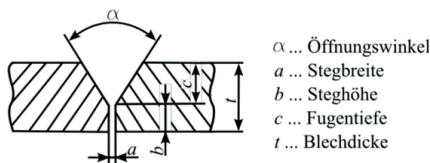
Nahtgeometrie einer einseitig ausgeführten Schweißnaht
